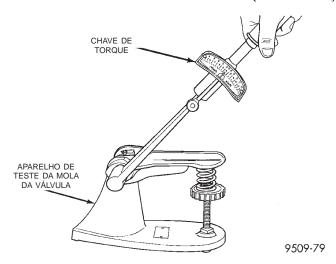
Teste da Mola da Válvula para Comprimento Comprimido
